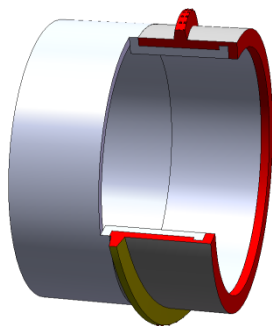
Корпус геохода с коаксиально расположенными секциями
